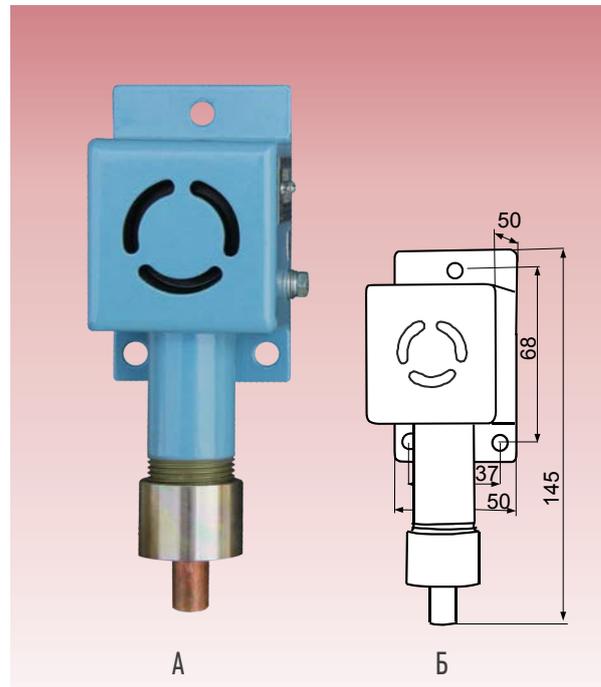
Сигнализатор ВС-6-5/24: А - внешний вид, Б - габаритные и установочные размеры.
